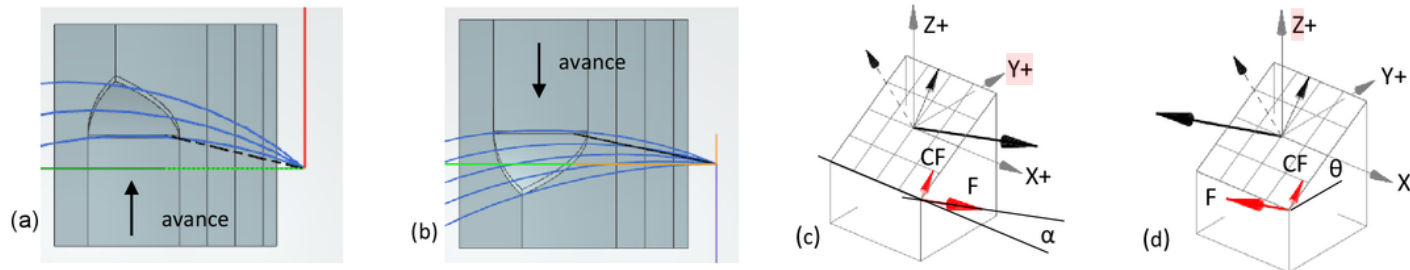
(a) Maquinado discordante. (b) Maquinado concordante. (c) Cinemática del maquinado discordante. (d) Cinemática del maquinado concordante. Fuente: Autores.
